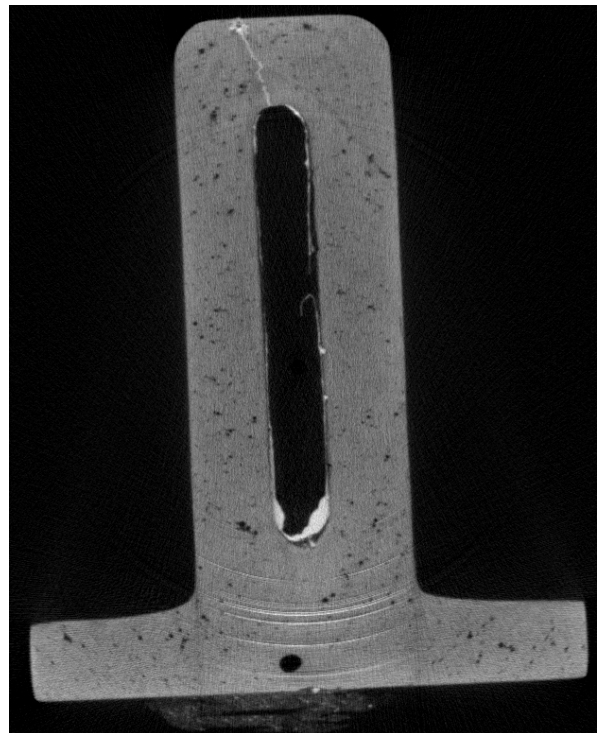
Sección de una pieza de cerámica con restos de fundición de aluminio. Se observa porosidad y una grieta rellena de fundición de aluminio.
